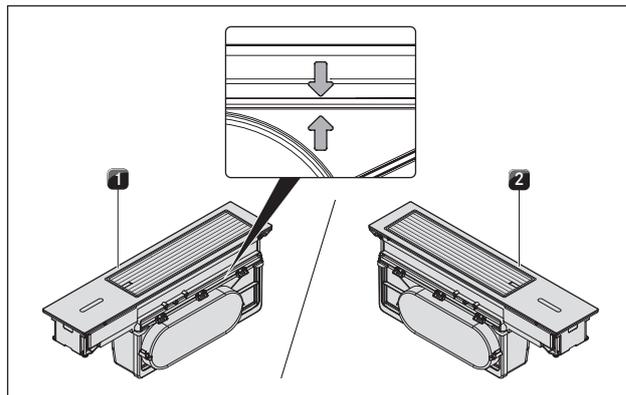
Exaustor de placa CKA2/CKA2AB montado
